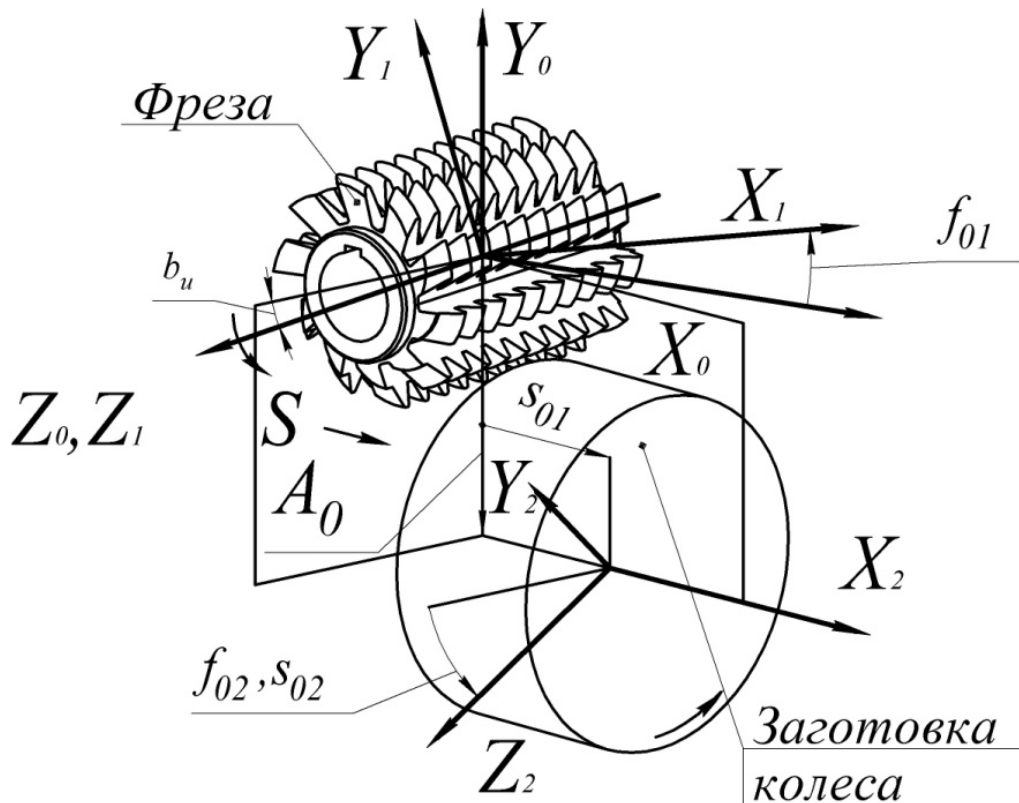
Розрахункова схема формоутворення косозубих зубчастих коліс черв'ячними фрезами
